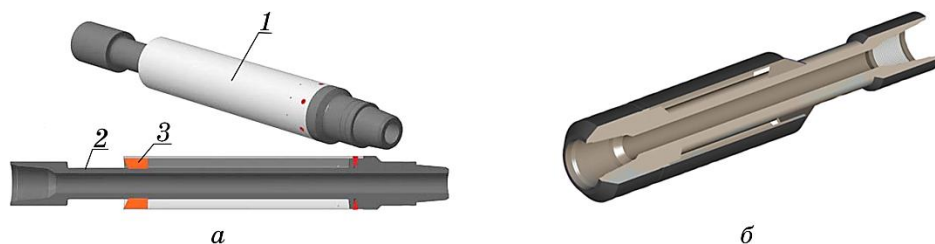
Шламоуловлювач: а — металевий (1 — кожух, 2 — корпус, 3 — центратор), б — струменевий.
